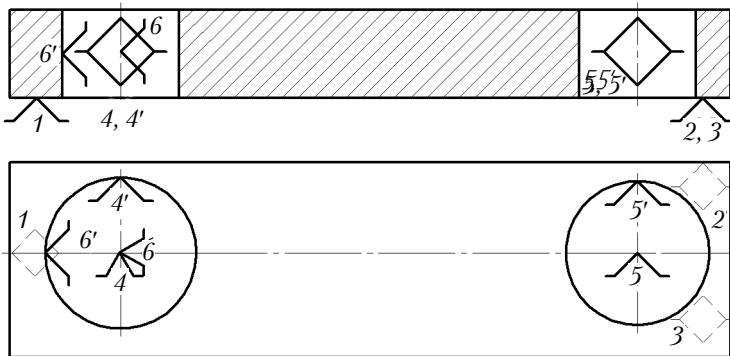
Теоретическая схема базирования заготовки, реализуемая установкой на плоскость и два установочных пальца
